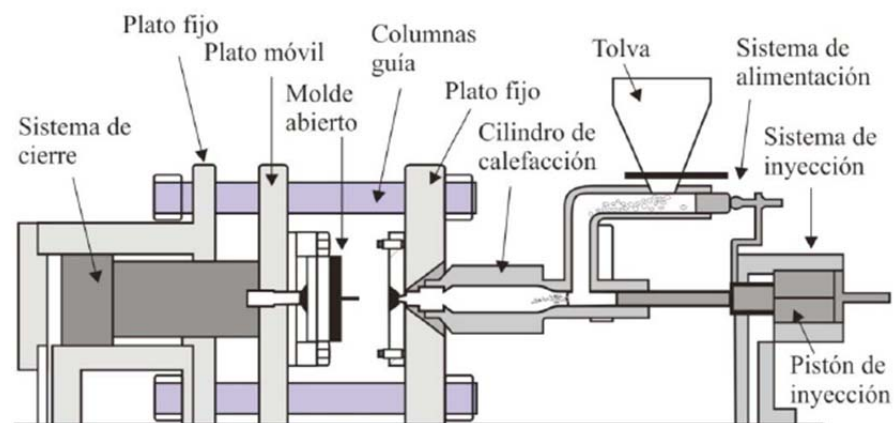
ESQUEMA DE UNA MÁQUINA DE MOLDEO POR INYECCIÓN CON PISTÓN [2].
